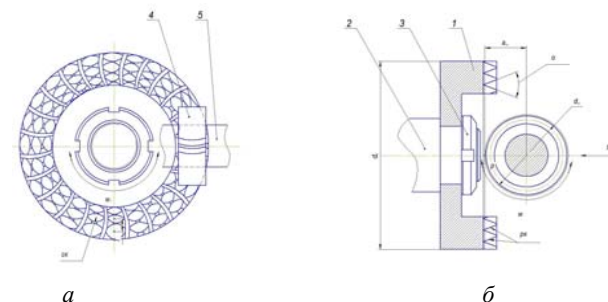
Схема способа обработки цилиндрических зубчатых колес шевингованием-прикатыванием: а – главный вид, б – вид сбоку
